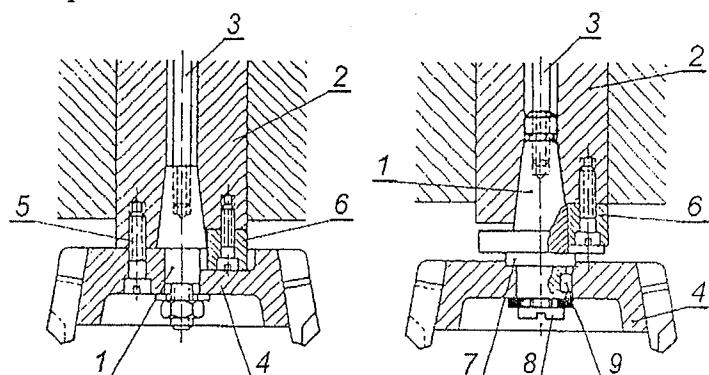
Montarea frezelor frontale cu alezaj pe arborele principal: (a) – fixare directă; (b) – fixare indirectă
